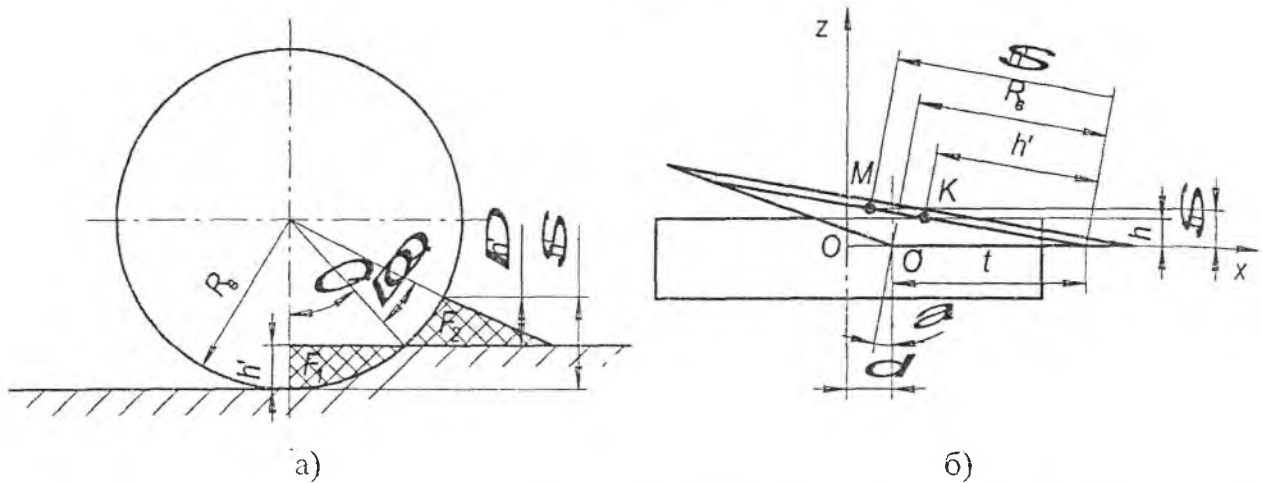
До визначення площі контакту валка із заготовкою із врахуванням пластичної хвилі
